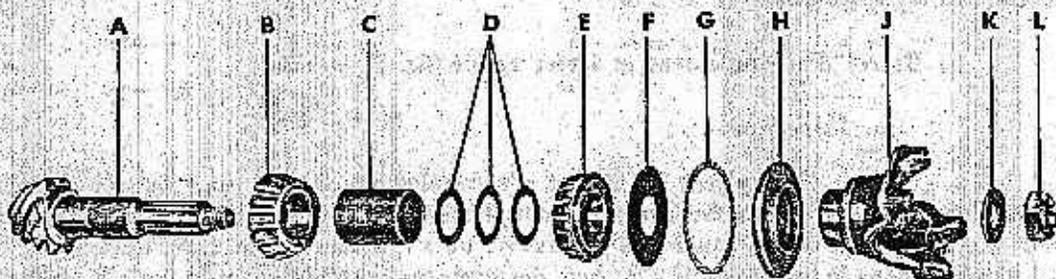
Ensemble du pignon d'attaque. Vue éclatée.
